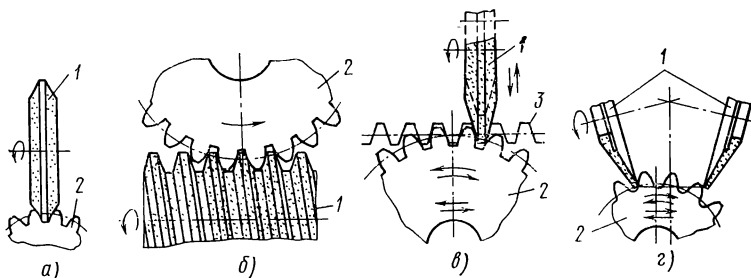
Методы зубошлифования цилиндрических зубчатых колес.
